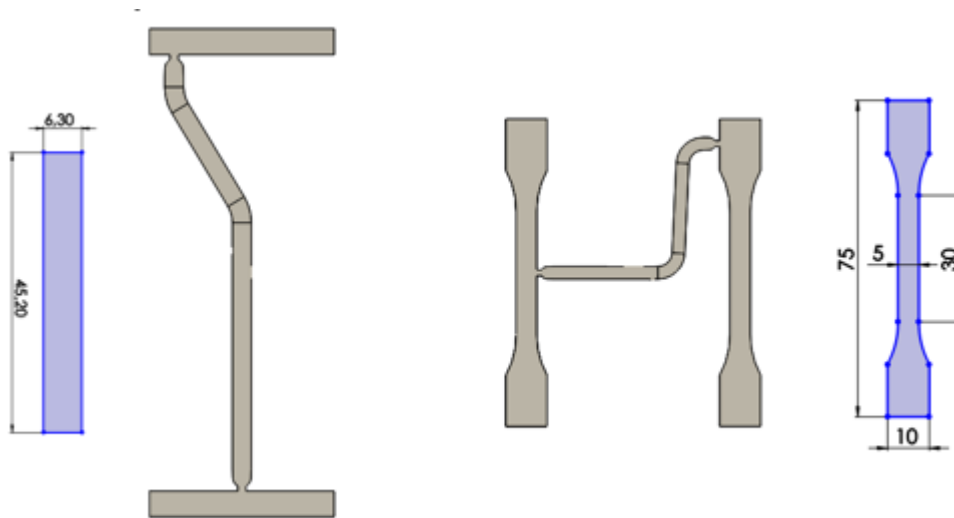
Desenho do sistema de alimentação de cada par de provetes de impacto (esquerda) e de tração (direita) e respectivas dimensões dos provetes.
